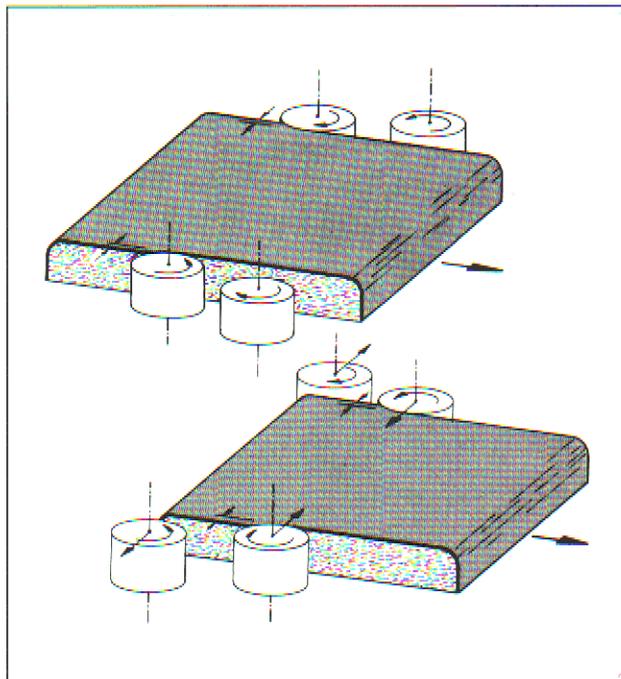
Schnittkantenbearbeitung mit einsetzgesteuerten Gleich- und Gegenlaufräsern
